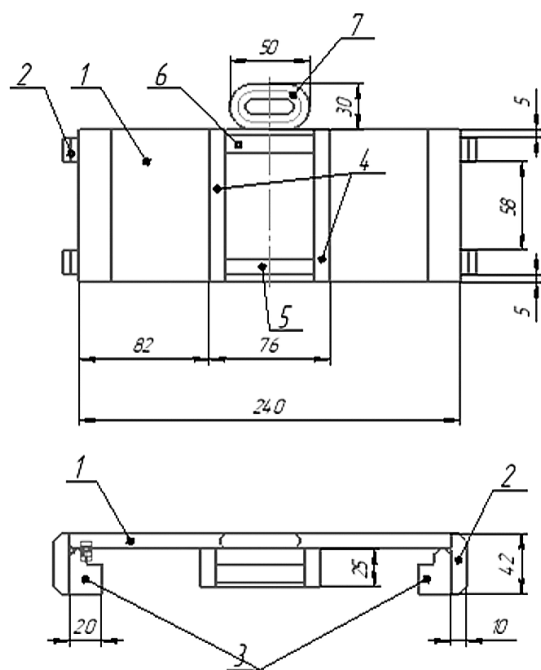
Съемный транцевый замок: 1 — стенка; 2 — усиление боковое; 3 — направляющая; 4 — ребро; 5 — распорка; 6 — распорка круглая; 7 — ручка
